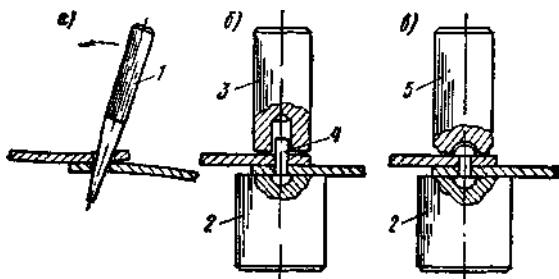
Инструменты для клепки: а — выравнивание отверстий в листах; б — осадка листов; в — формирование замыкающей головки
